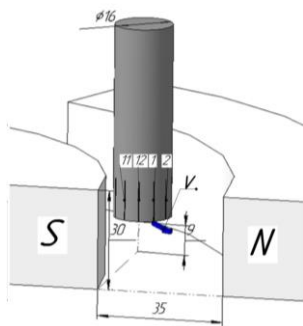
Схема расположения образцов с контрольными зонами в магнитной рабочей зоне
